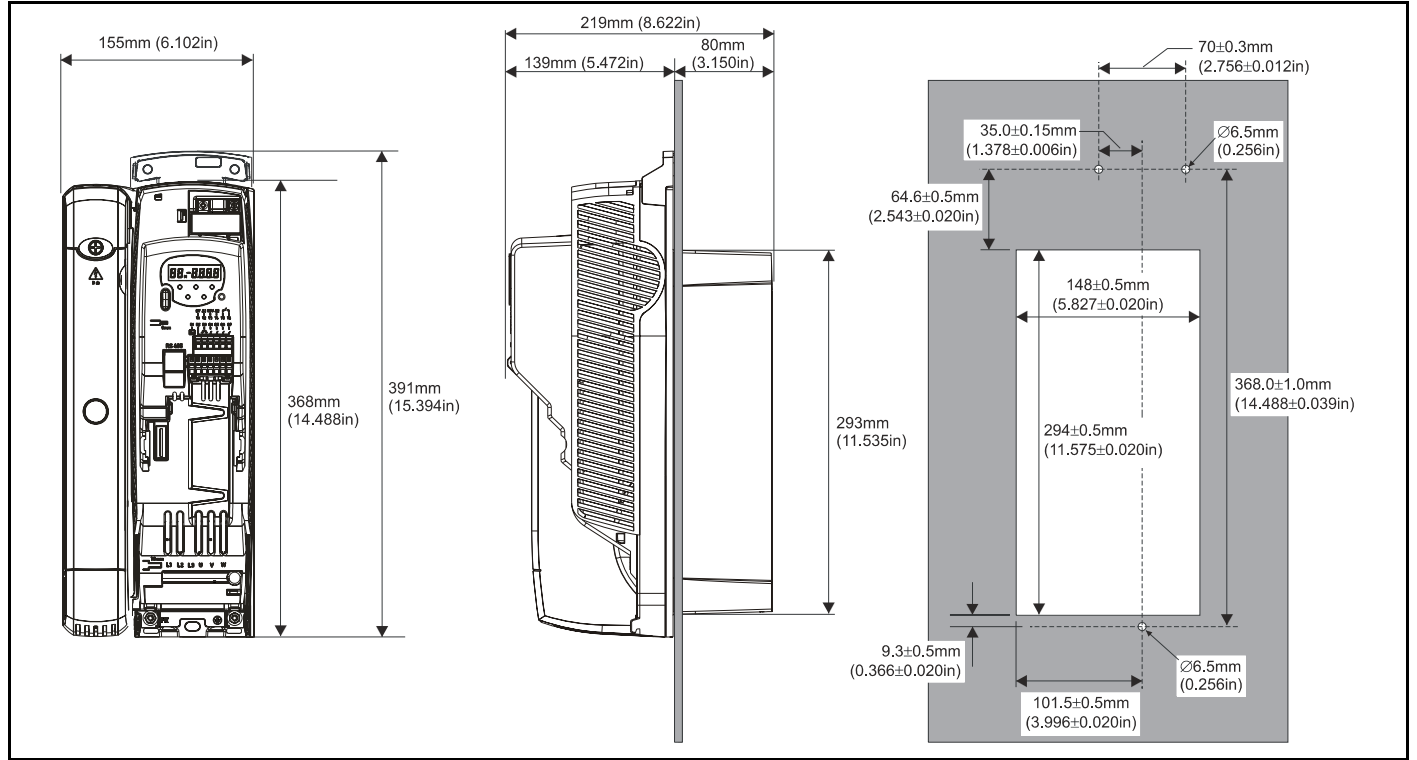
Boy 6 sürücülerin yüze montajı
